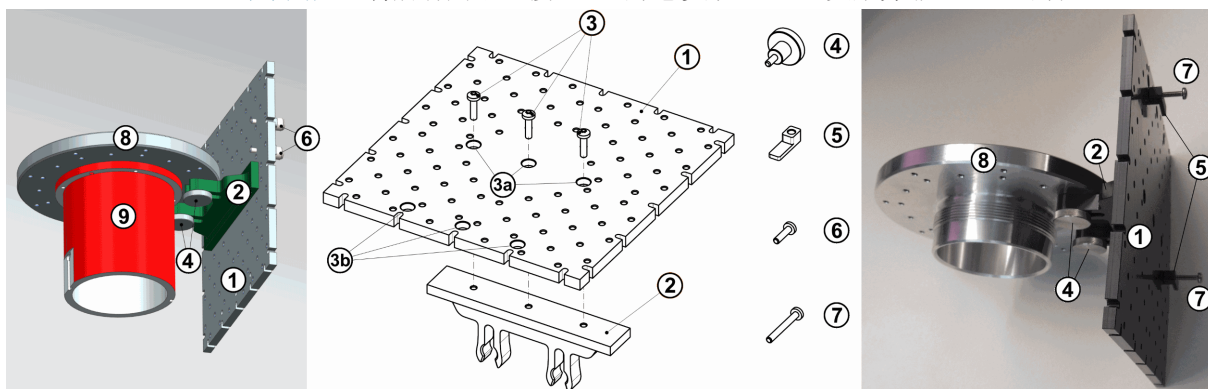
用于承载 DUT 和印刷电路板 (PCB) 的支架装置
